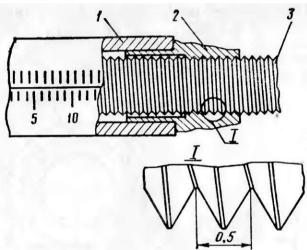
Устройство винтовой пары: 1 — стебель; 2 — резьбовая втулка; 3 — микровинт
